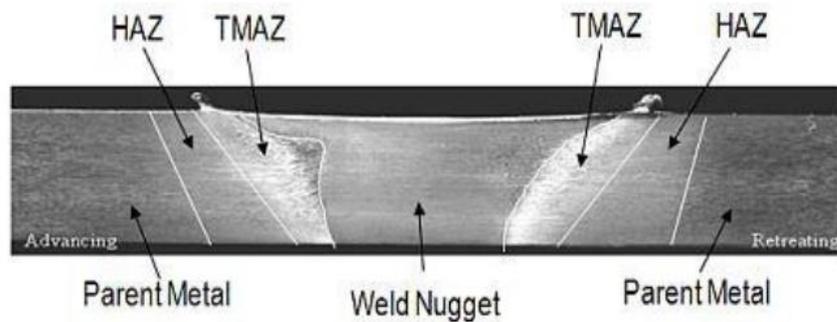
friction linier welding (www.twi-global.com)
